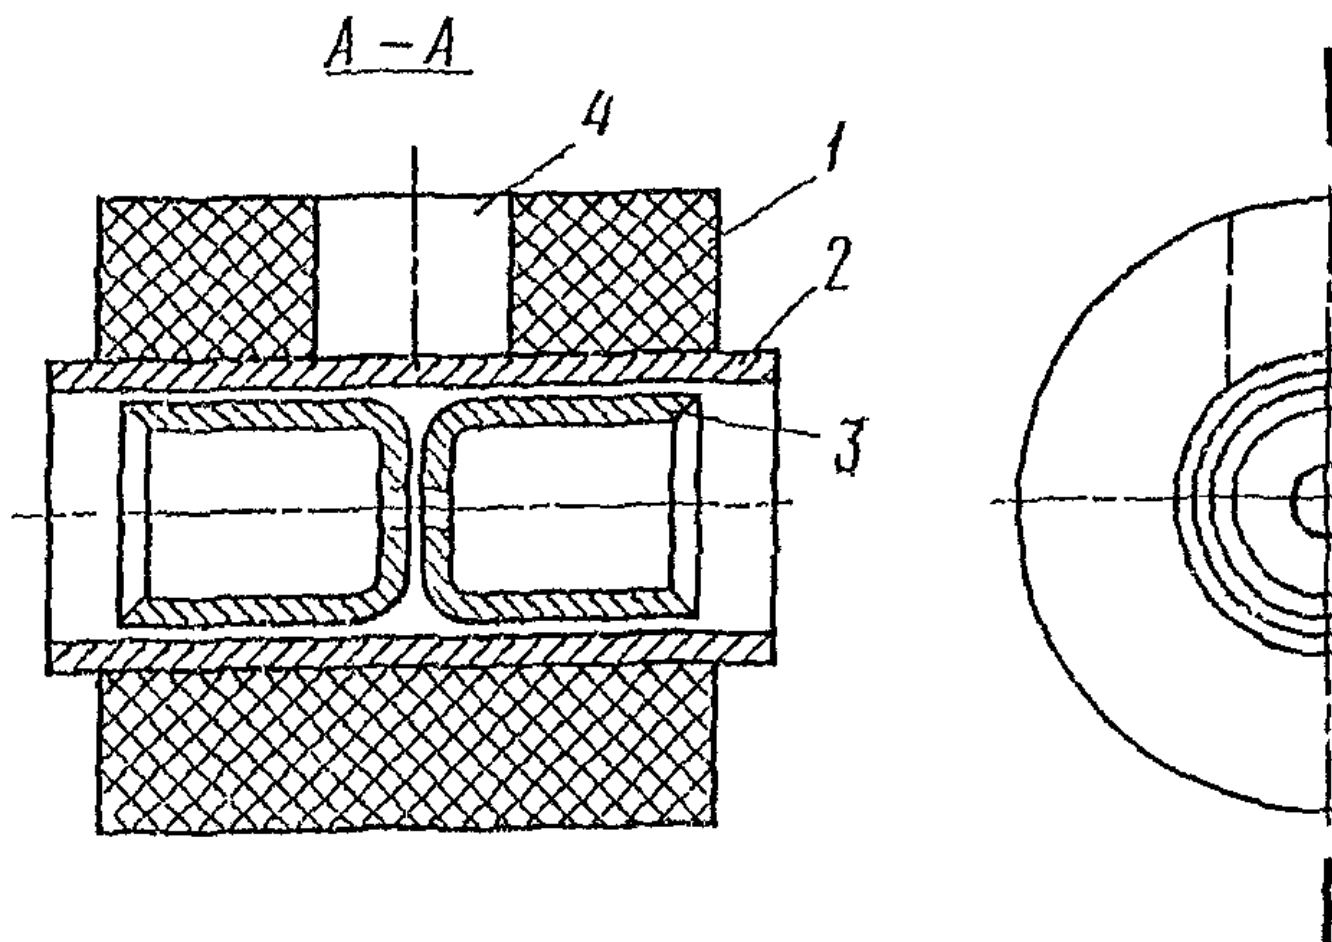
Термитный патрон марки ПА: 1 - термитный муфель; 2 - стальной кокиль (формочка); 3 - алюминиевый колпачок; 4 - литниковое отверстие
